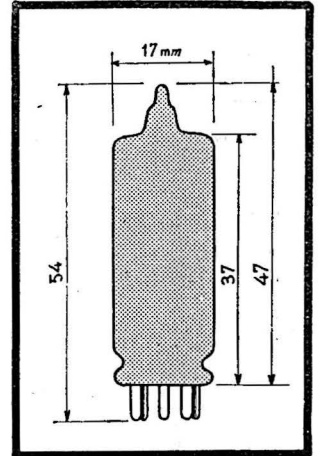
Fig. F. — Dimensions des tubes chauffés sous 6 et 12 V.
